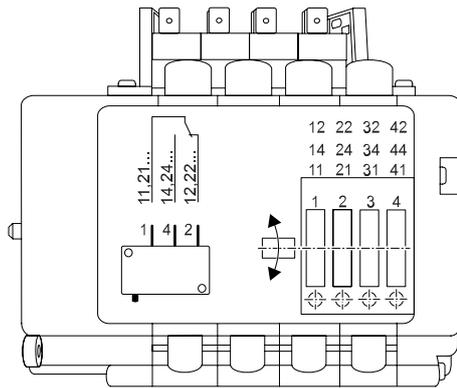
Final de carrera de engranajes giratorio de 4 pasos
